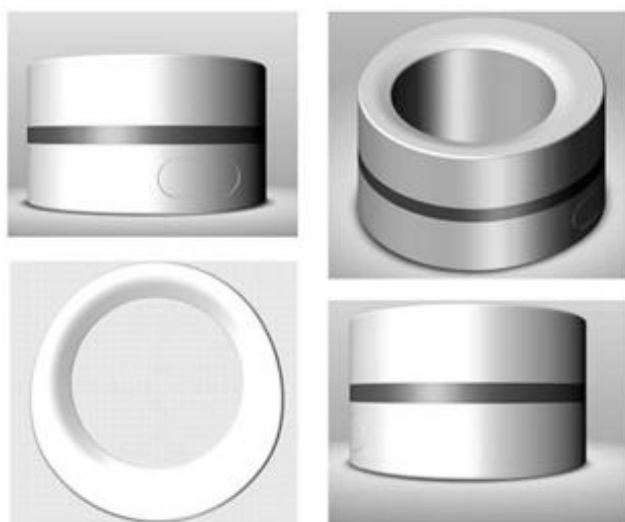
Модель корпуса устройства размеров 20 мм.
